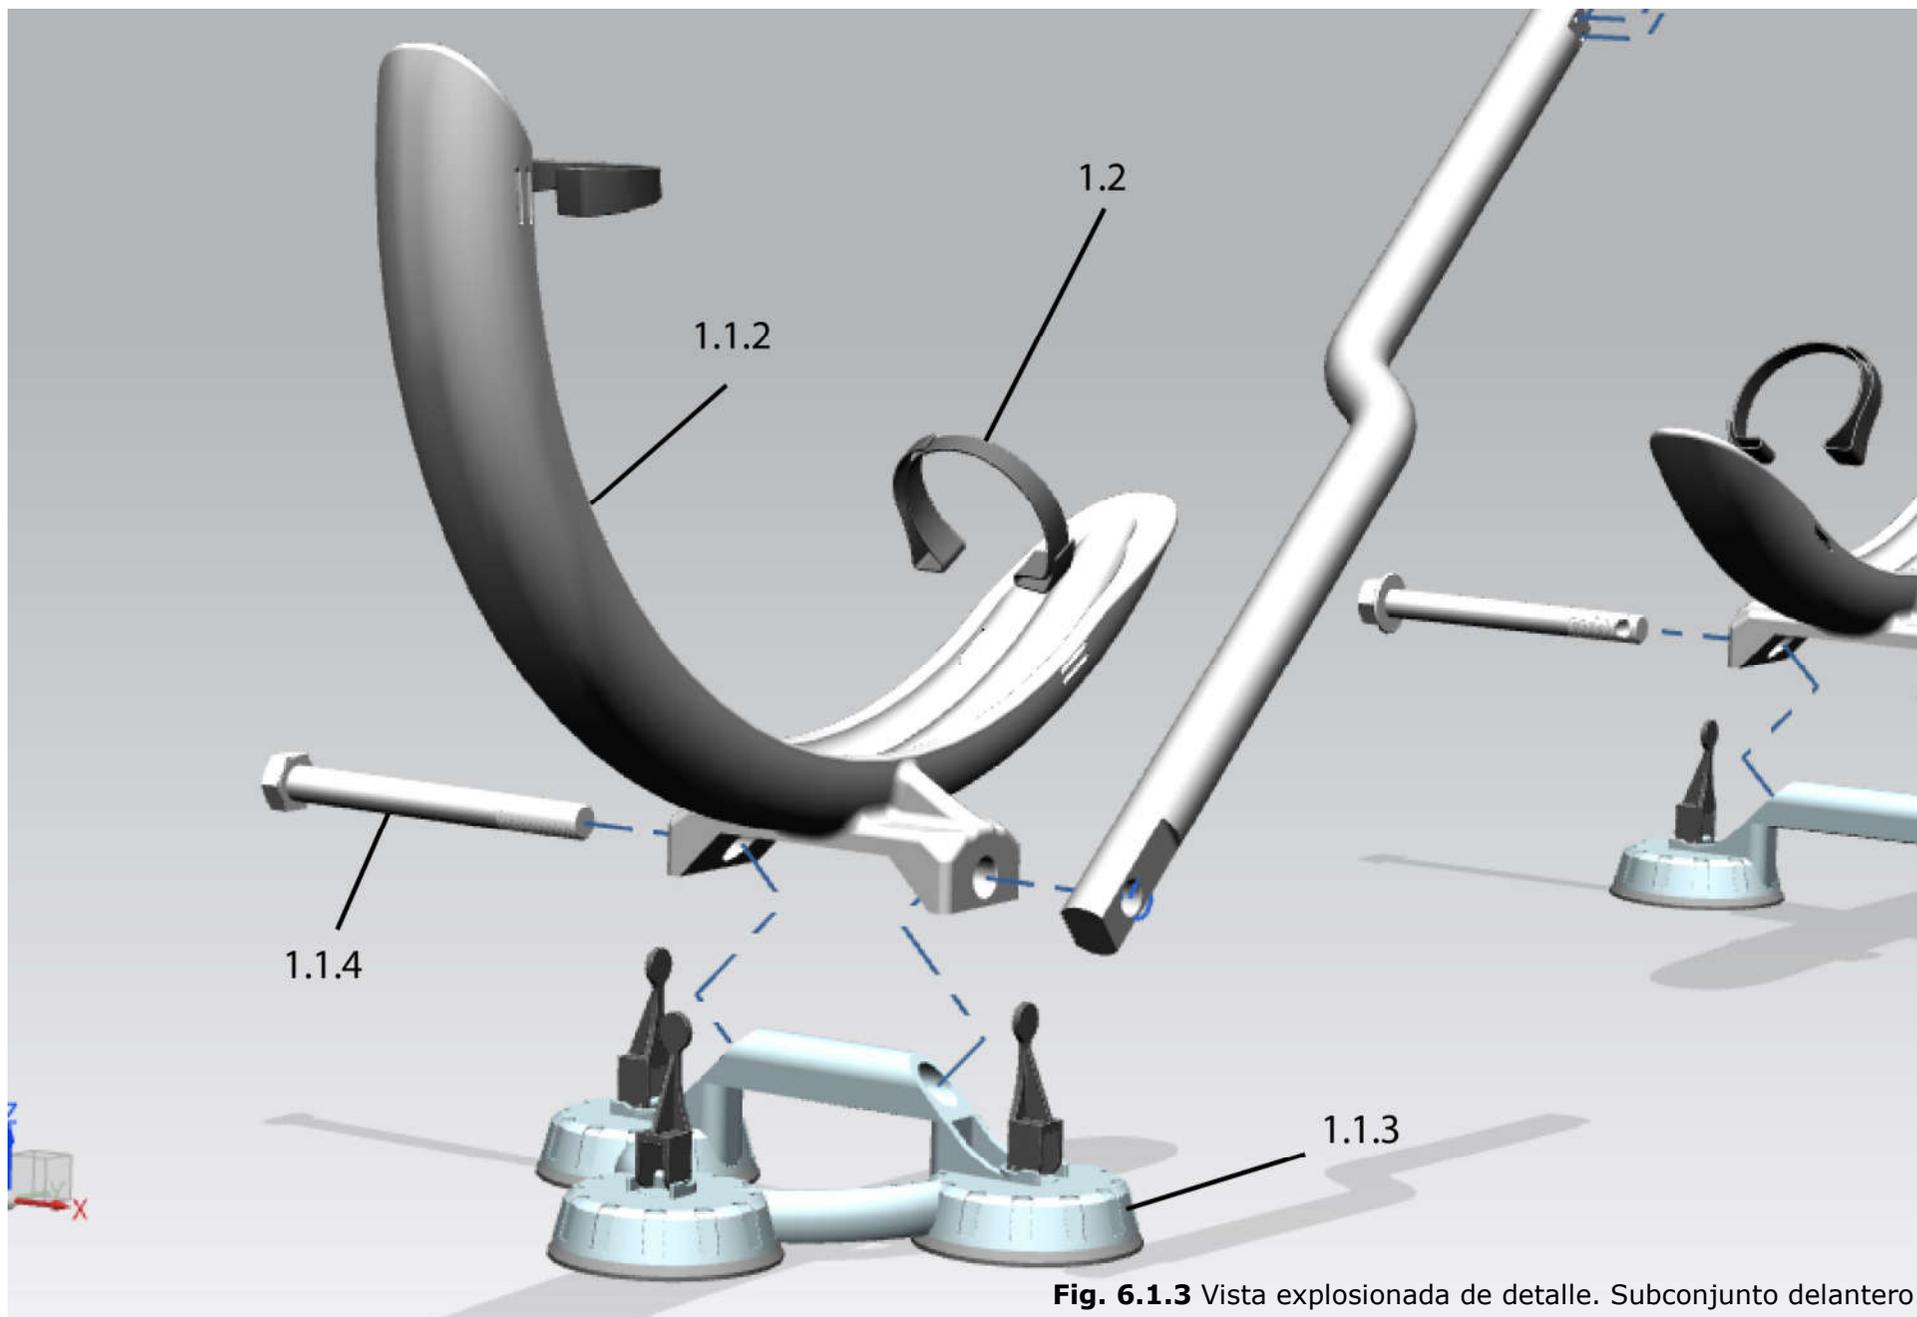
Vista explosionada de detalle. Subconjunto delantero.
